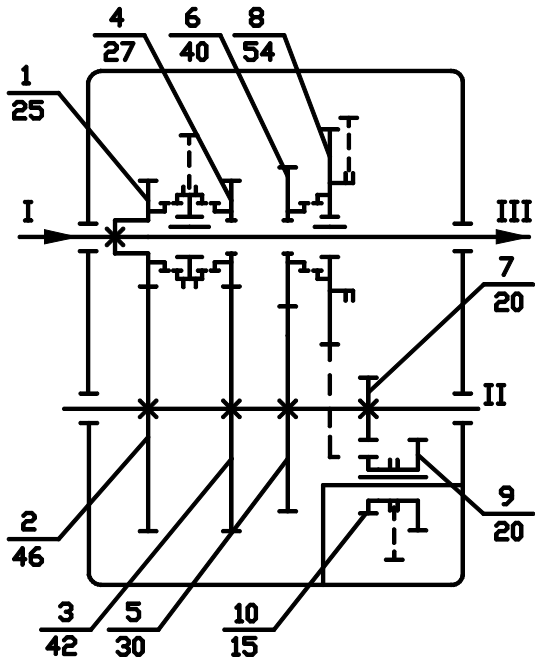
Коробка передач ГАЗ-53 (ГАЗ-66)
